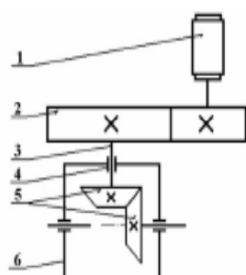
Кинематическая схема привода с коническим зубчатым редуктором
